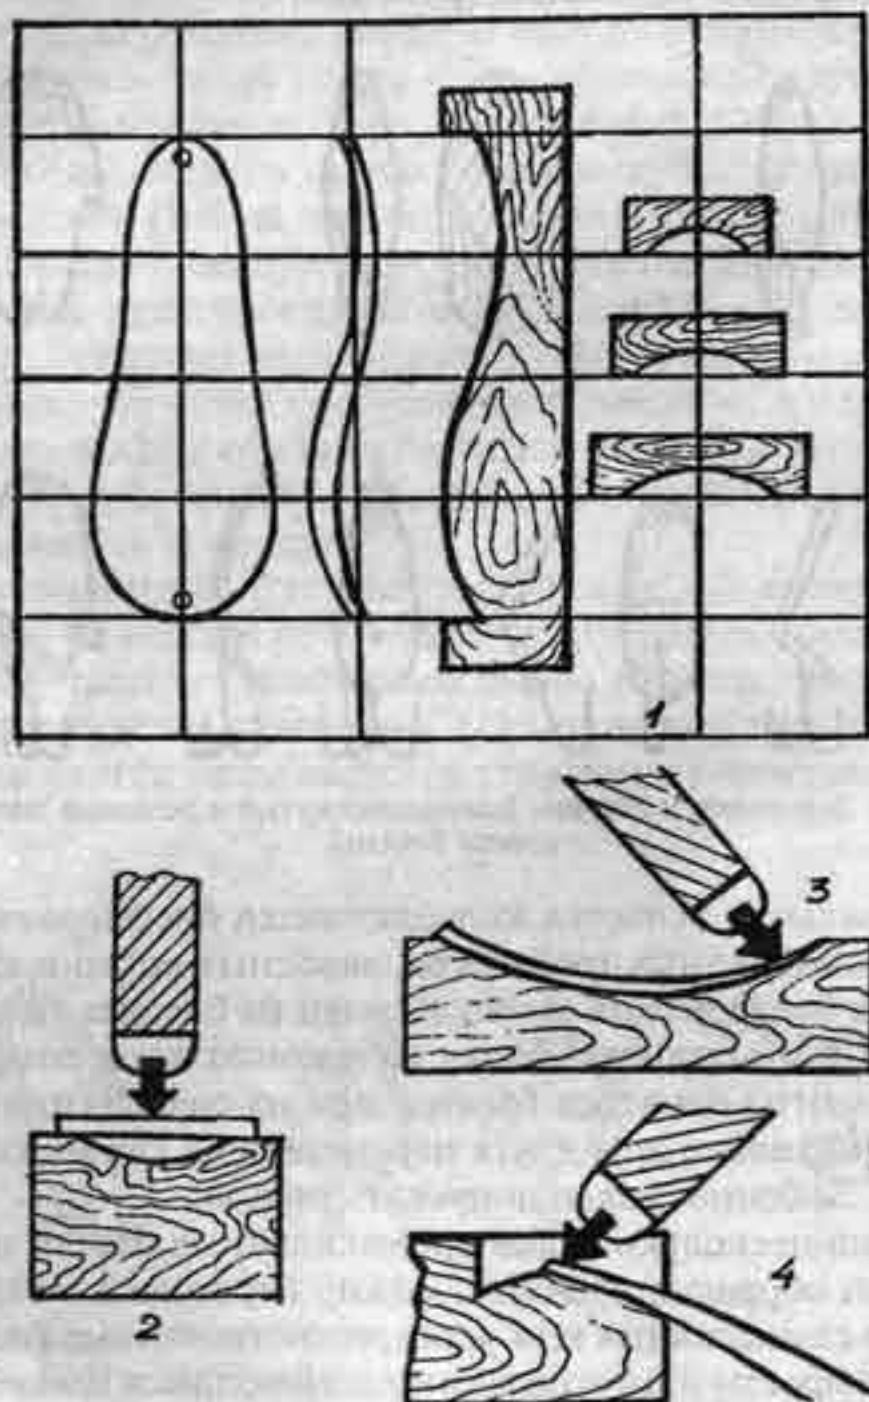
Технология изготовления блесны «Шторлек»: 1 — матрица; 2, 3, 4 — этапы изготовления блесны.
